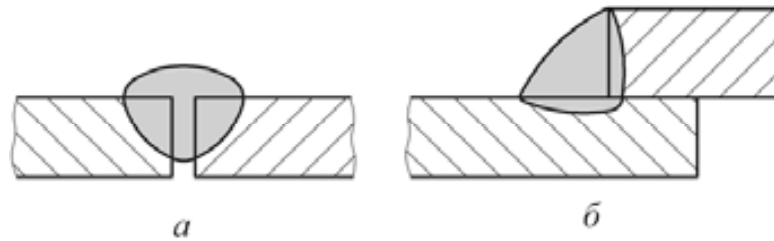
Вид сварных швов по форме поперечного сечения:
